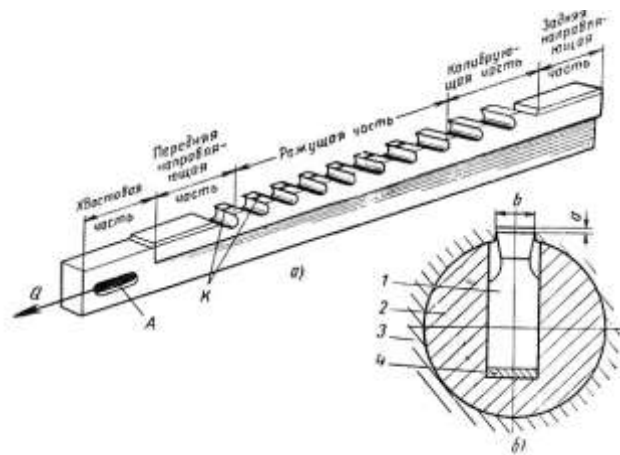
Схема протягивания шпоночного паза: а - шпоночная протяжка; б - схема резания: 1 - протяжка; 2 - направляющая втулка; 3 - заготовка; 4 – прокладка
